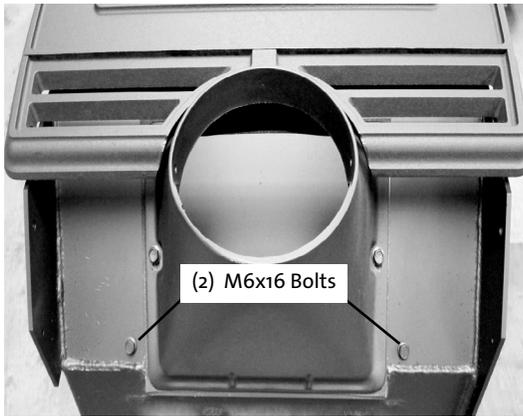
Enlever (2) boulons M6x16 de l'arrière
